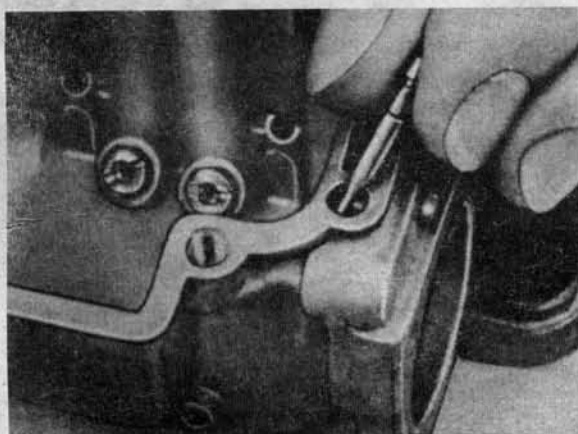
Карбюратор Weber 32 DIR – калибровочный винт и главные топливные жиклеры
